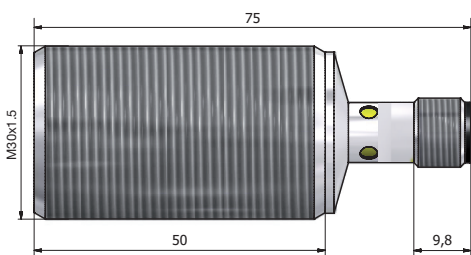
Lange Ausführung, bündiger Einbau, Steckversion
